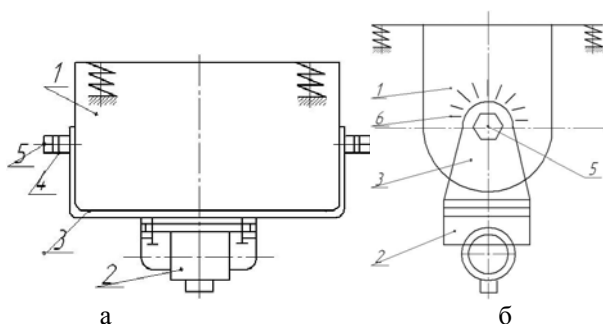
Принципова схема модифікованого вібраційного верстата ВНУ-100: а – загальний вид; б – вид збоку
